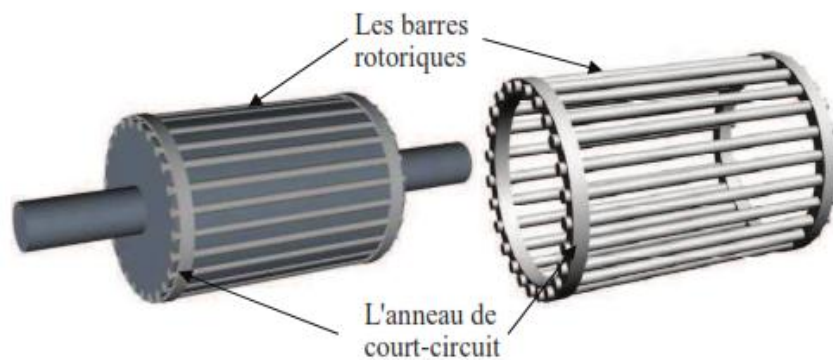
Rotor de la machine asynchrone triphasé à cage d'écureuil [3].
